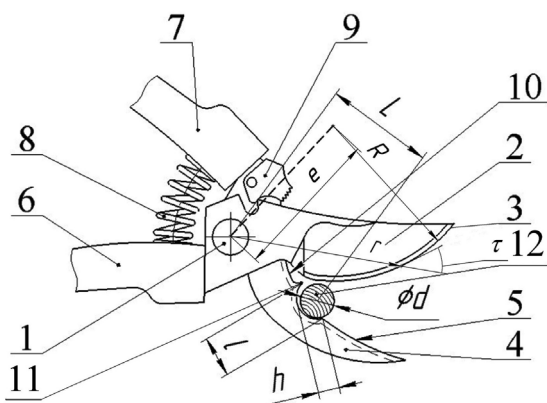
Конструктивная схема лезвийной пары секатора: 1 – шарнир; 2 – режущий нож; 3 – лезвие режущего ножа; 4 – противорежущий нож; 5 – рабочая поверхность противорежущего ножа; 6, 7 – рукоятки; 8 – пружина; 9 – замок; 10 – барьерное возвышение; 11 – начало выреза; 12 – срезаемая лоза; d – диаметр перерезаемой лозы; l – длина выреза на противорезном ноже; h – глубина выреза на противорежущем ноже; L – расстояние от выреза до оси шарнира; R – радиус эксцентрической окружности; r – радиус-вектор сегмента режущего ножа; e – эксцентриситет; τ – угол резания
